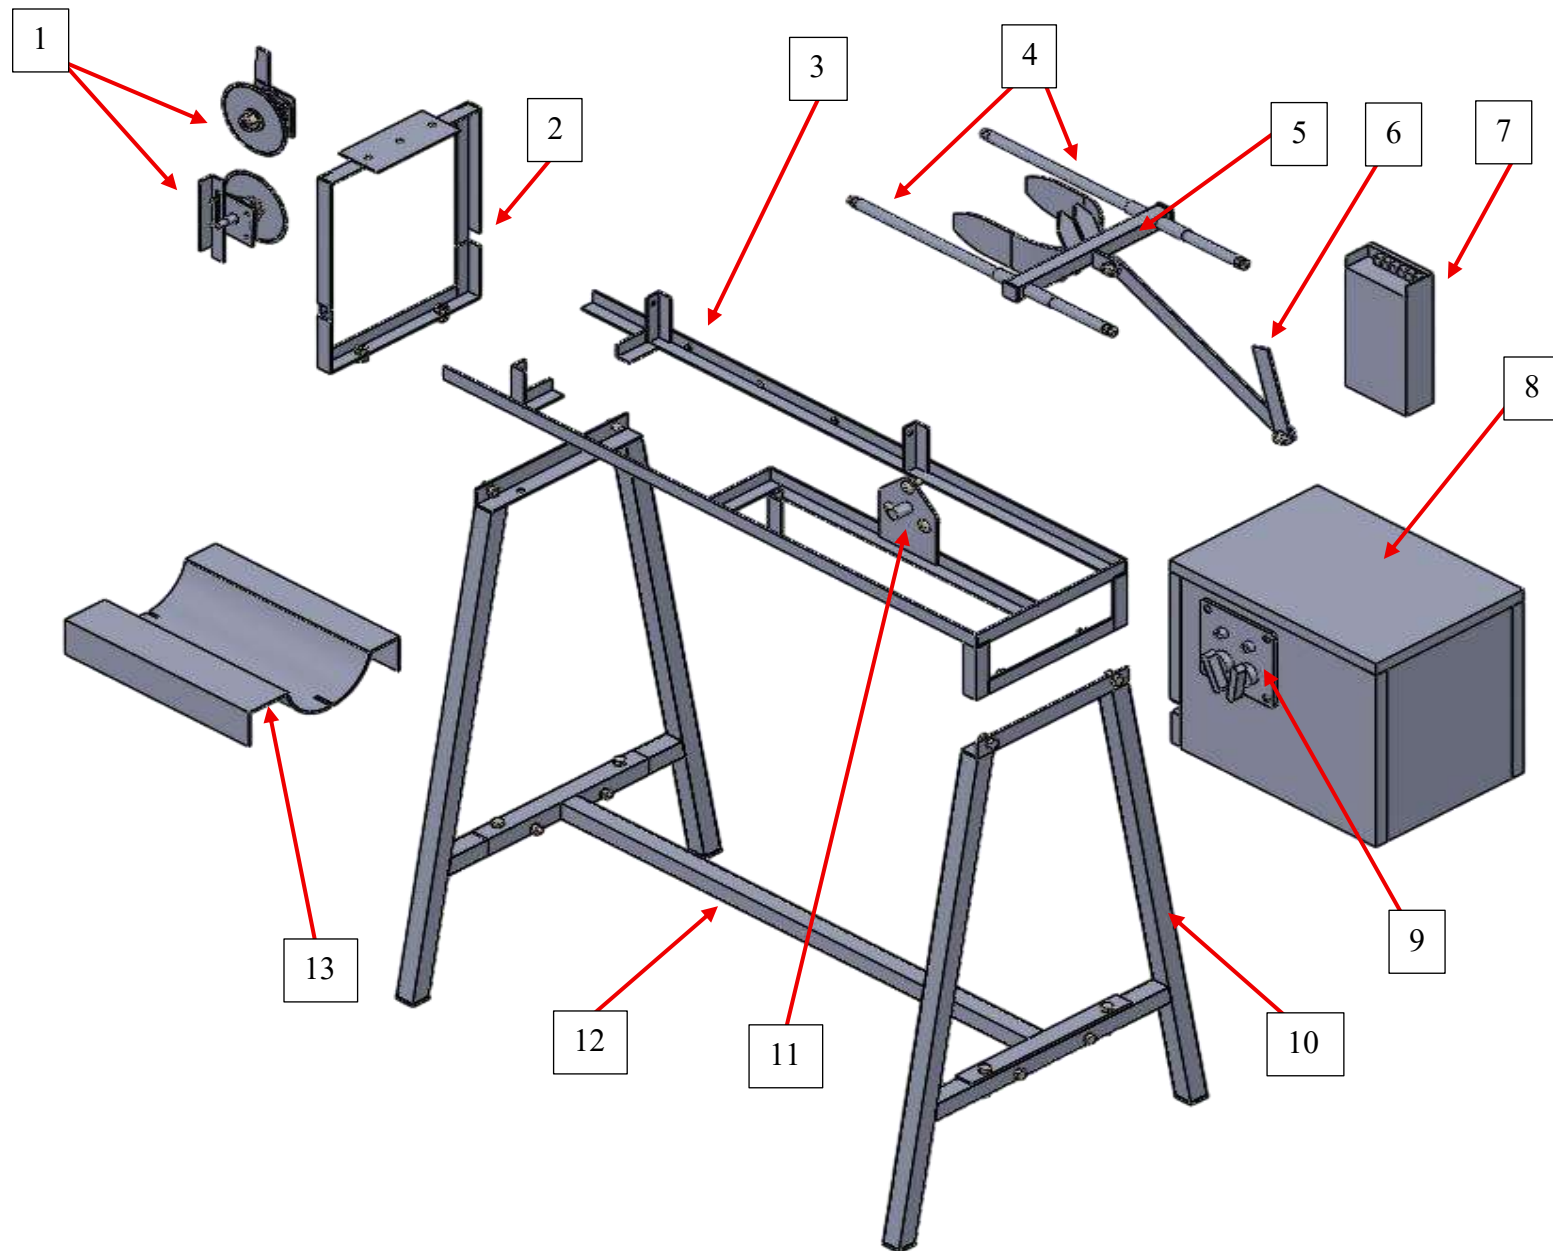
Vista en explosión de la desvainadora de cacao
